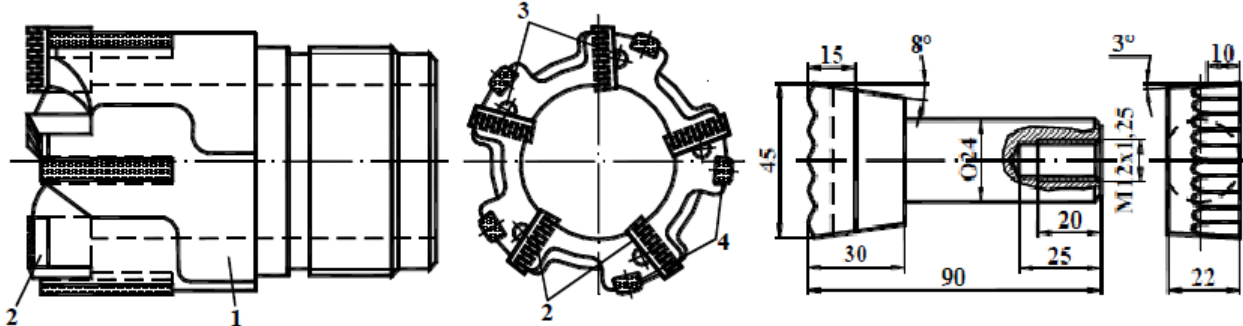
П'яти різцеве свердло-коронка типу ТСТ (НМ) Ruco MBL \varnothing 290 мм із зовнішнім відведенням стружки для кільцевого свердлення, що працює за принципом ділення ширини стружки, урівноважене. 1 - корпус; 2 - різці; 3 - клини; 4 - направляючі елементи.
